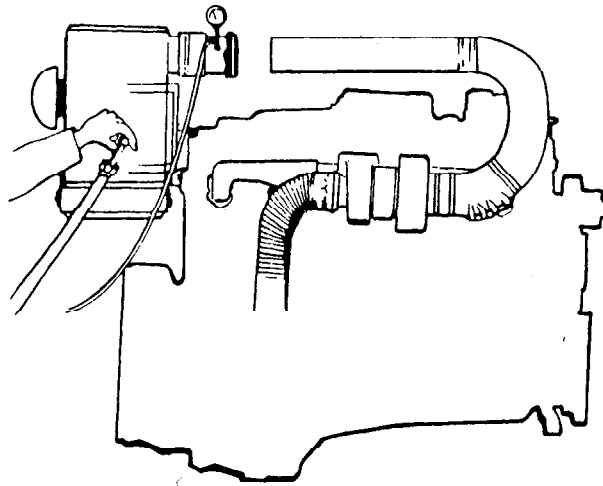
Conexiones para probar si hay fugas por el filtro de aire en un motor turbocargado
